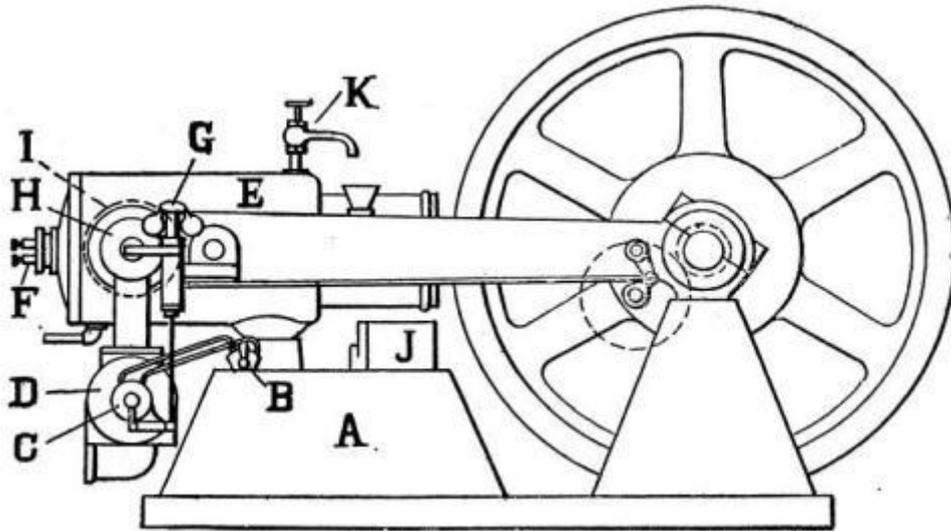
Двигатель Пристманна, топливный бак, из которого давлением воздуха вытеснялось топливо, обозначен литерой «А»
